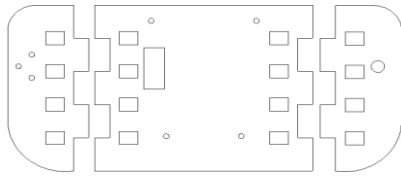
2 Chassis tank (sumber: bukalapak.com)
